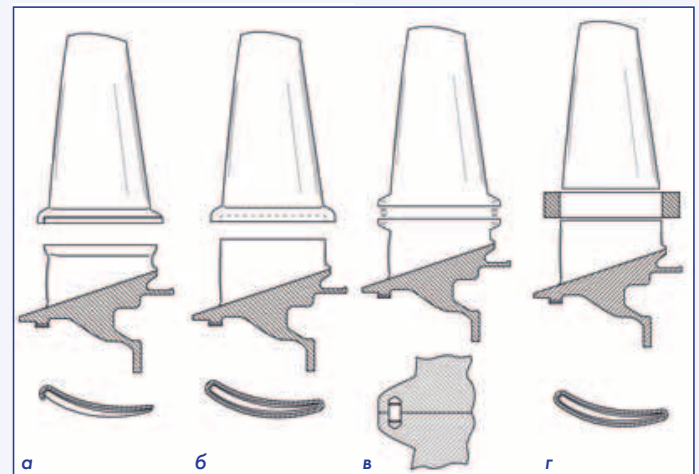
Метод ремонта монокоилс, имеющих укороченные лопатки: а) сварка лопатки "в колодец", неполное перекрытие; б) сварка лопатки "в колодец", полное перекрытие; в) сварка в кольце; г) фиксация лопатки штифтами
